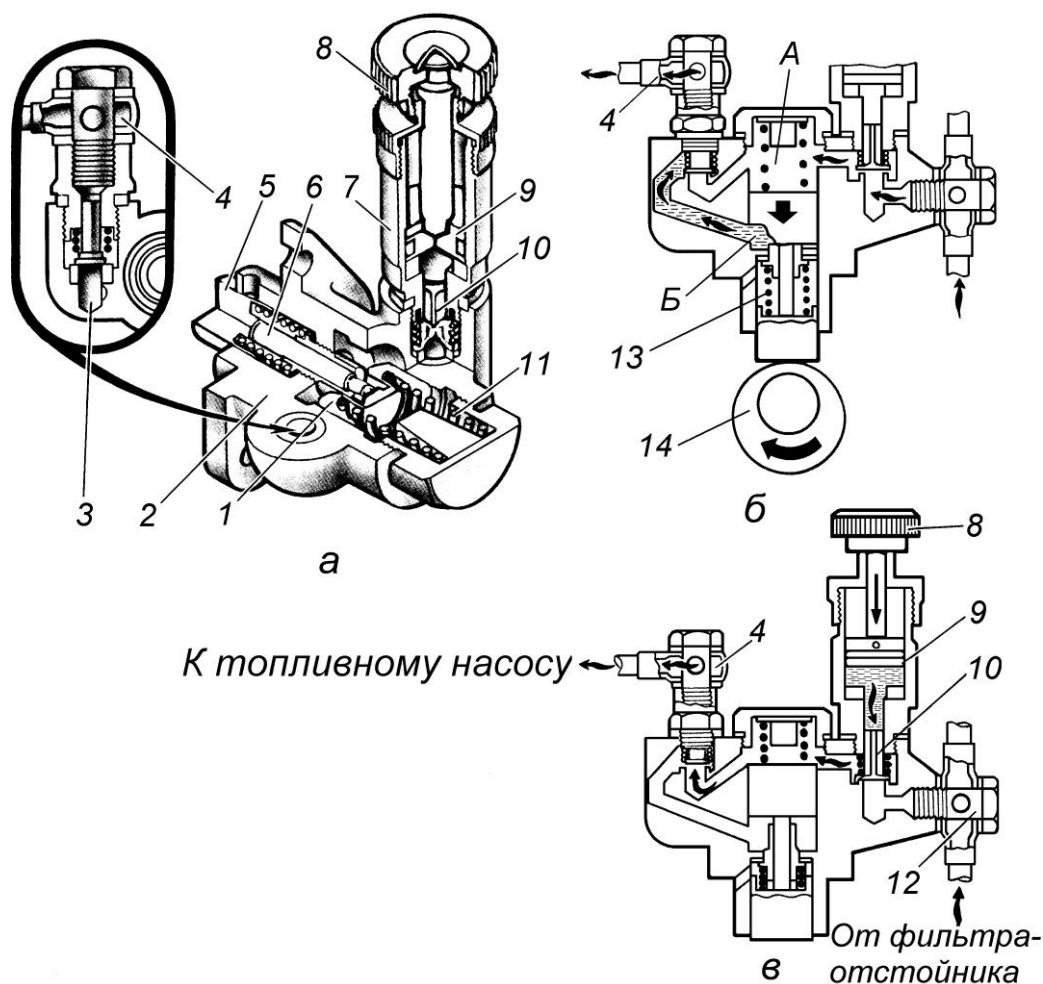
Подкачивающий насос (насос низкого давления ТННД):
